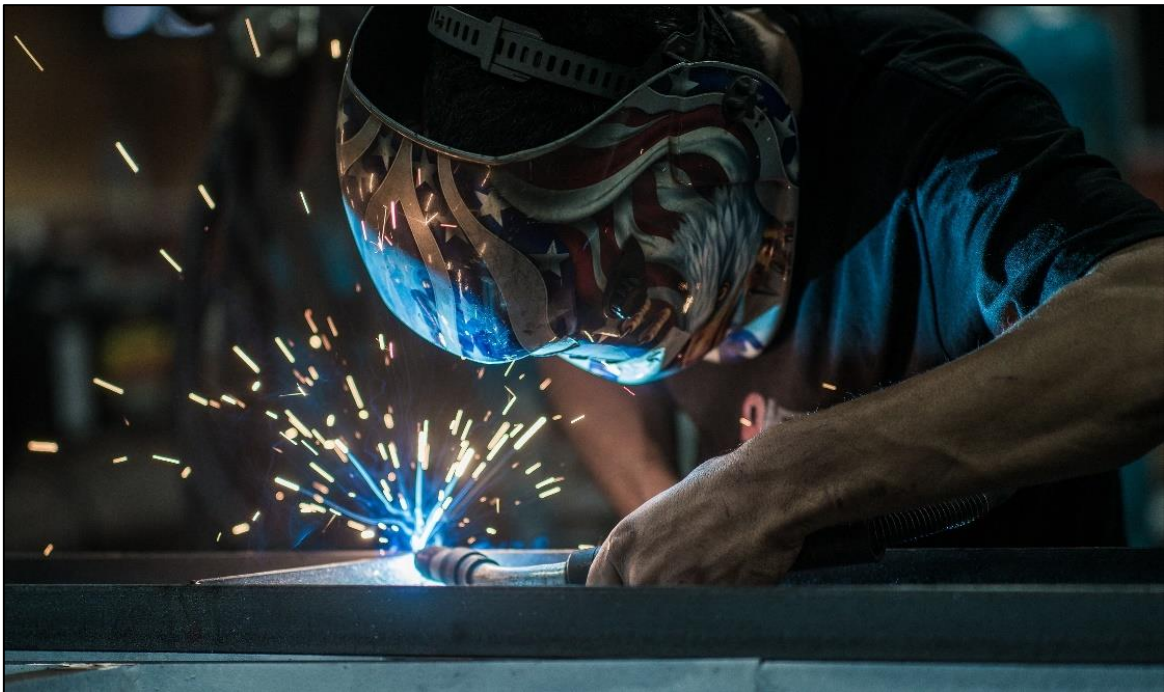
Soldador aplicando proceso GMAW en apuntalamiento de estructura liviana
